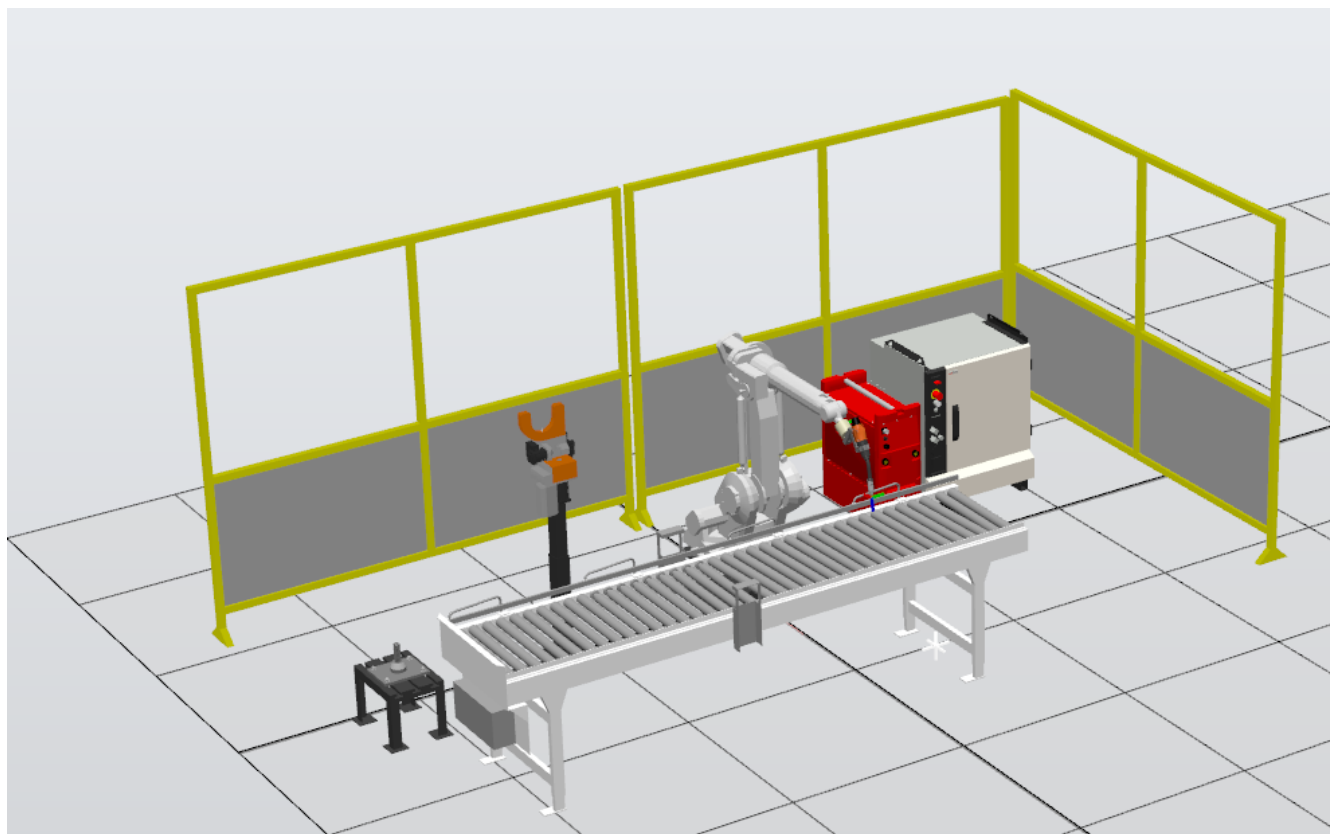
Загальний вигляд зварювальної комірки СМТ зварювання роботом IRB 1520ID-4-150-02
